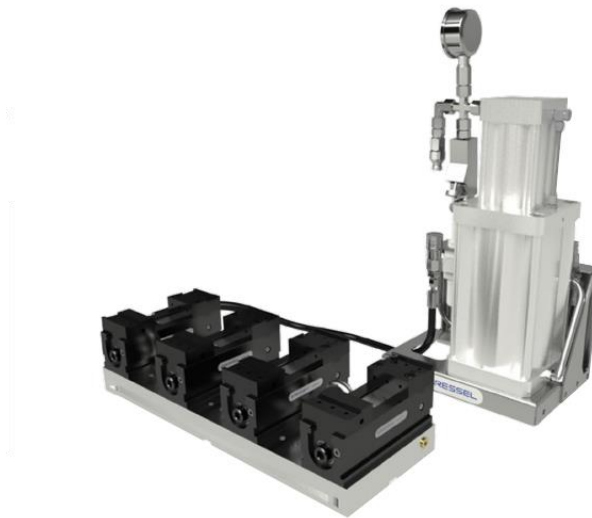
Pneumaticko-hydraulický systém DESTACO [16]
